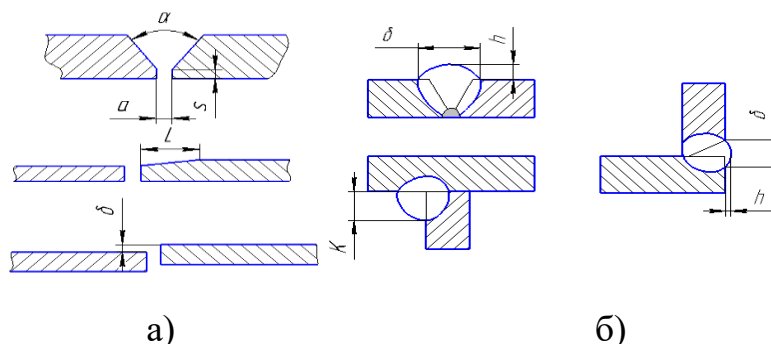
Элементы геометрической формы подготовки кромок под сварку (а) и шва (б): v - ширина шва, h - высота шва, K - катет шва [20].
